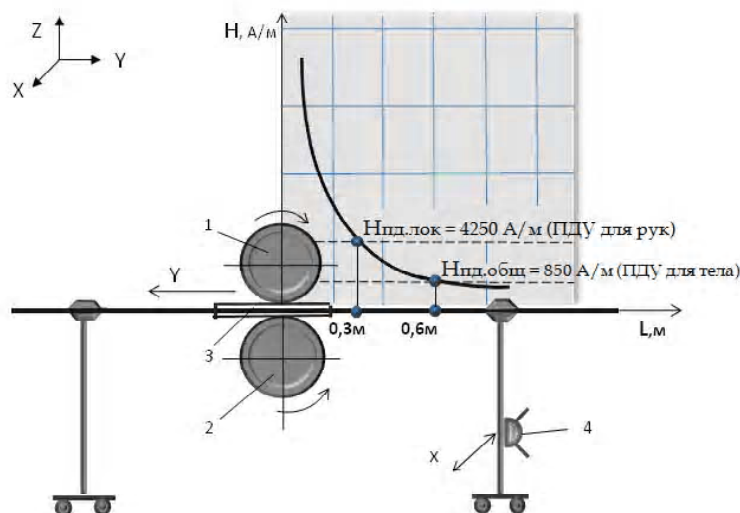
Схема приспособления для сварки металлокомпозитных заготовок:
